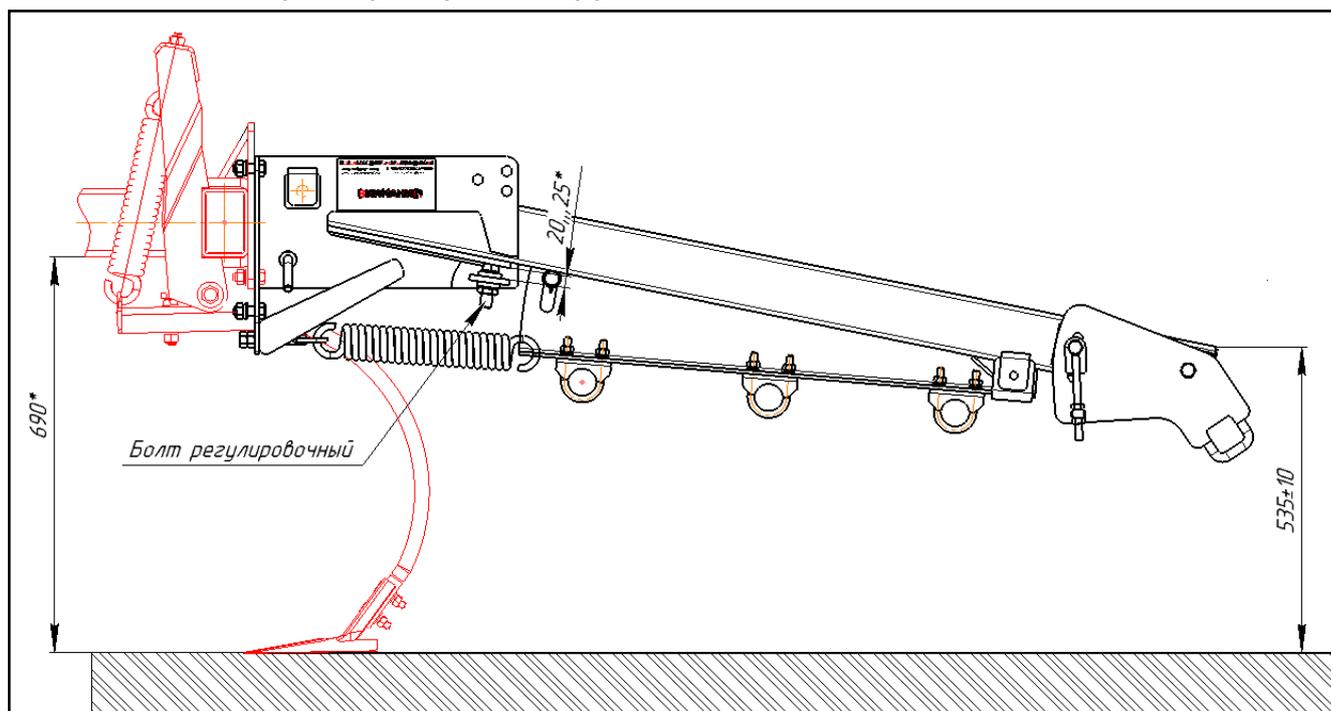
Установка подвесок комбинированного шлейфа
